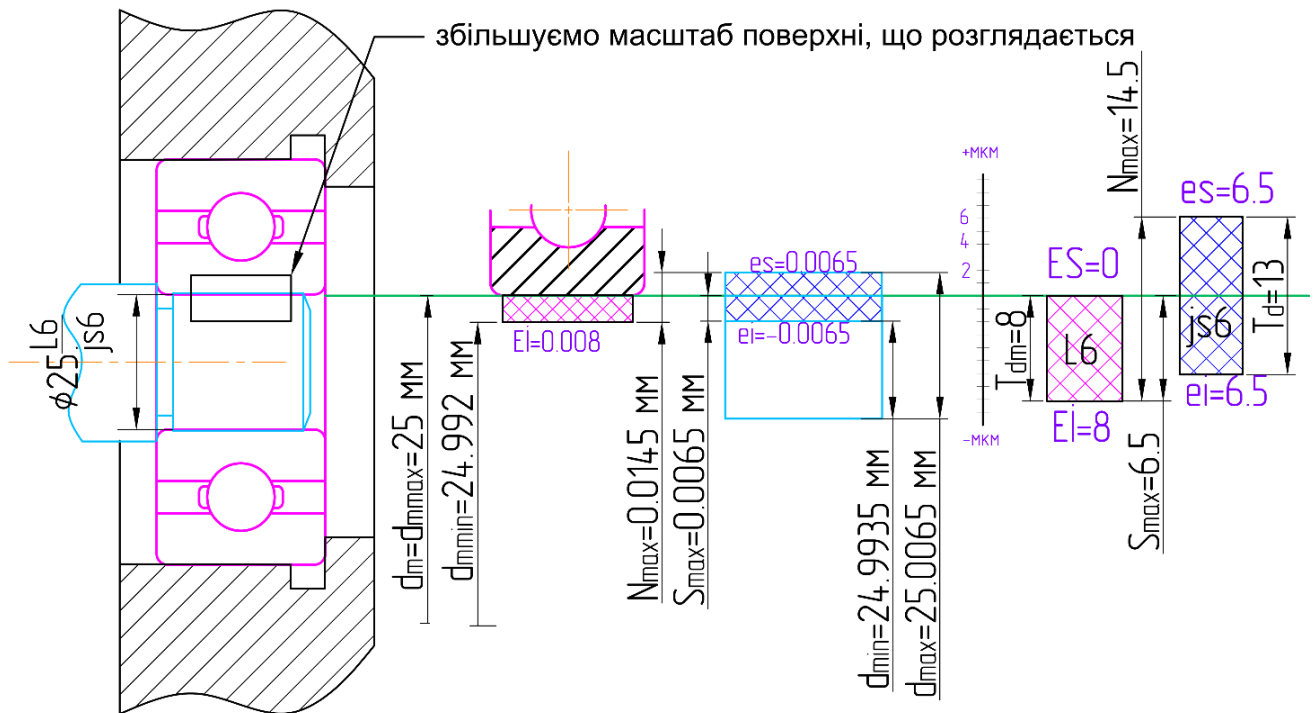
Схема розташування полів допусків для з'єднання підшипника з валом $\varnothing 25 \frac{L6}{js6}$ (*Виконується на форматі А1 див. додаток Б2)
